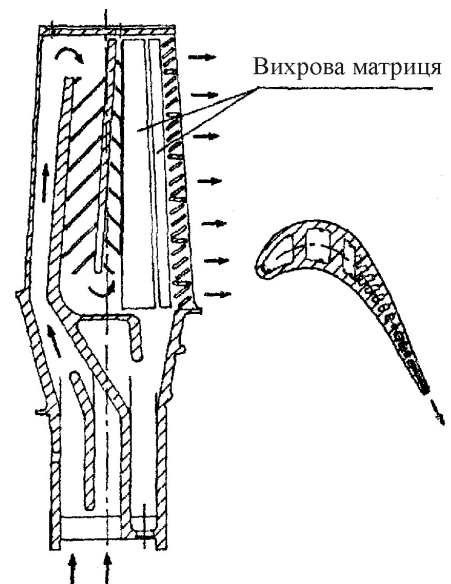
Конструкція охолоджуваної робочої лопатки з вихровою матрицею
